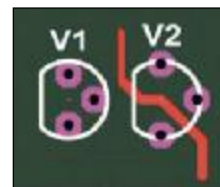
Verschieben von Pads an einem TO-92-Gehäuse
